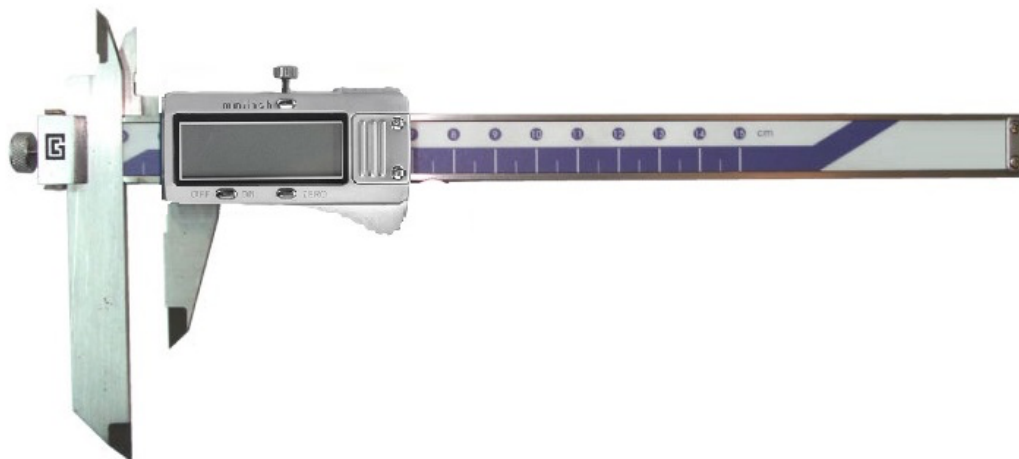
Общий вид штангенциркулей модели ШЦЦС-123
